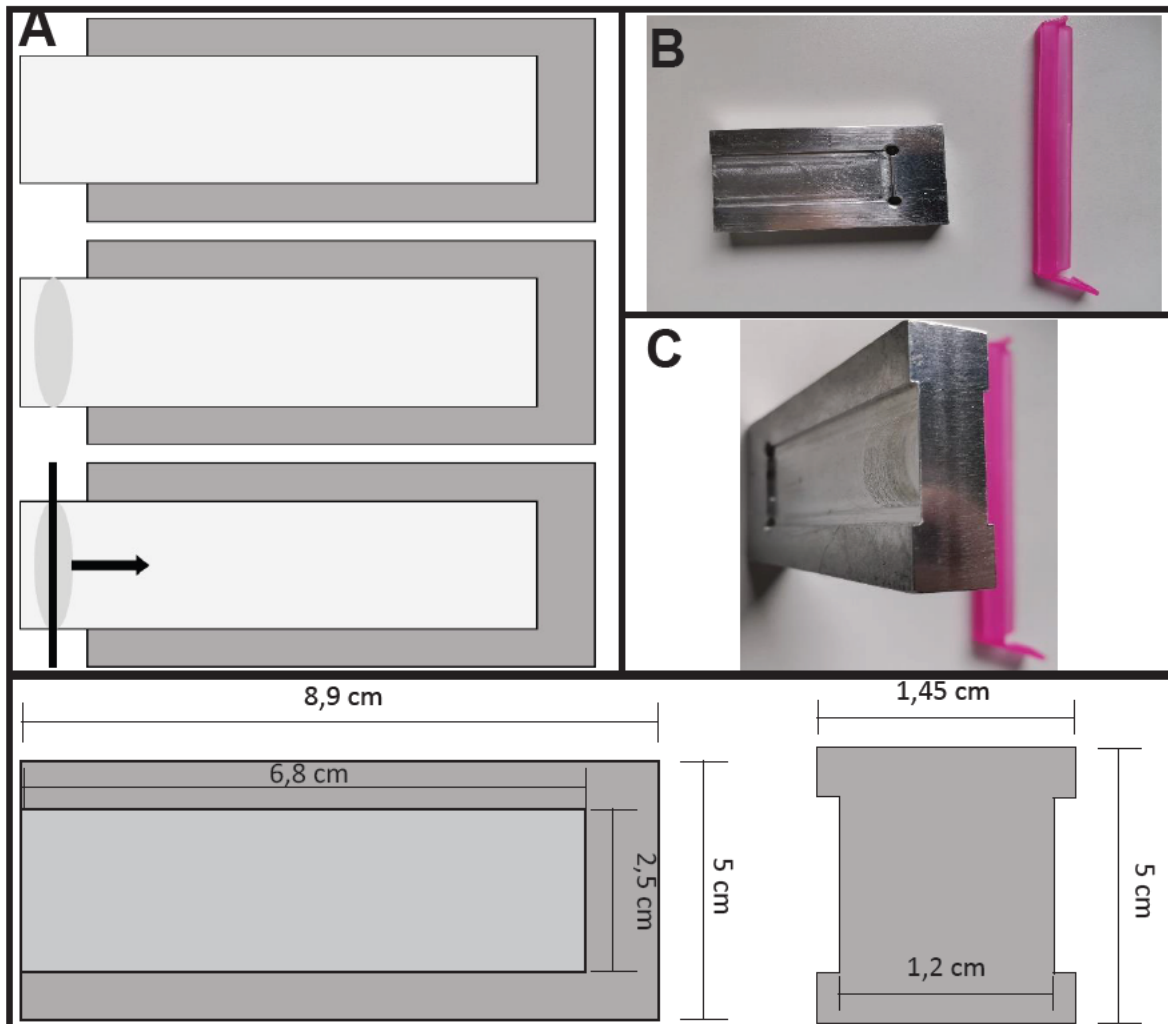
Beschichtung der Objektträger. A: Verfahren der Beschichtung. B: Draufsicht der Fassung zur Beschichtung. C: Frontansicht der Fassung zur Beschichtung. D: Maße der Fassung zur Beschichtung
